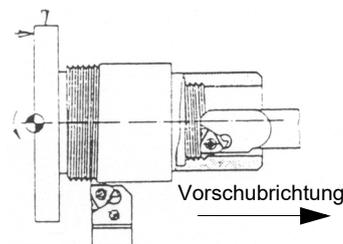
Linksgewinde bei Rechtslauf der Maschinenspindel
